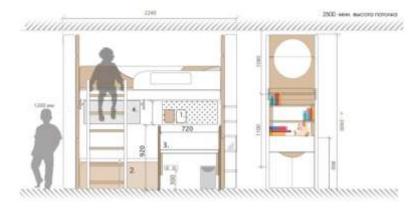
Эскиз сборки №3. Кровать - чердак
